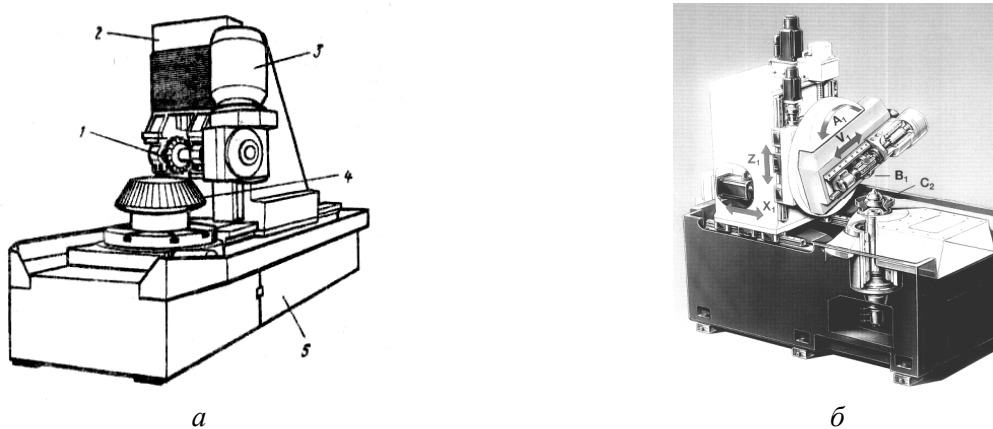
Загальний вигляд верстатів для нарізання конічних коліс за неперервного обкочування за РК-способом: а – універсальний зубофрезерний верстат; б – зубофрезерний верстат з ЧПК мод. LC80
